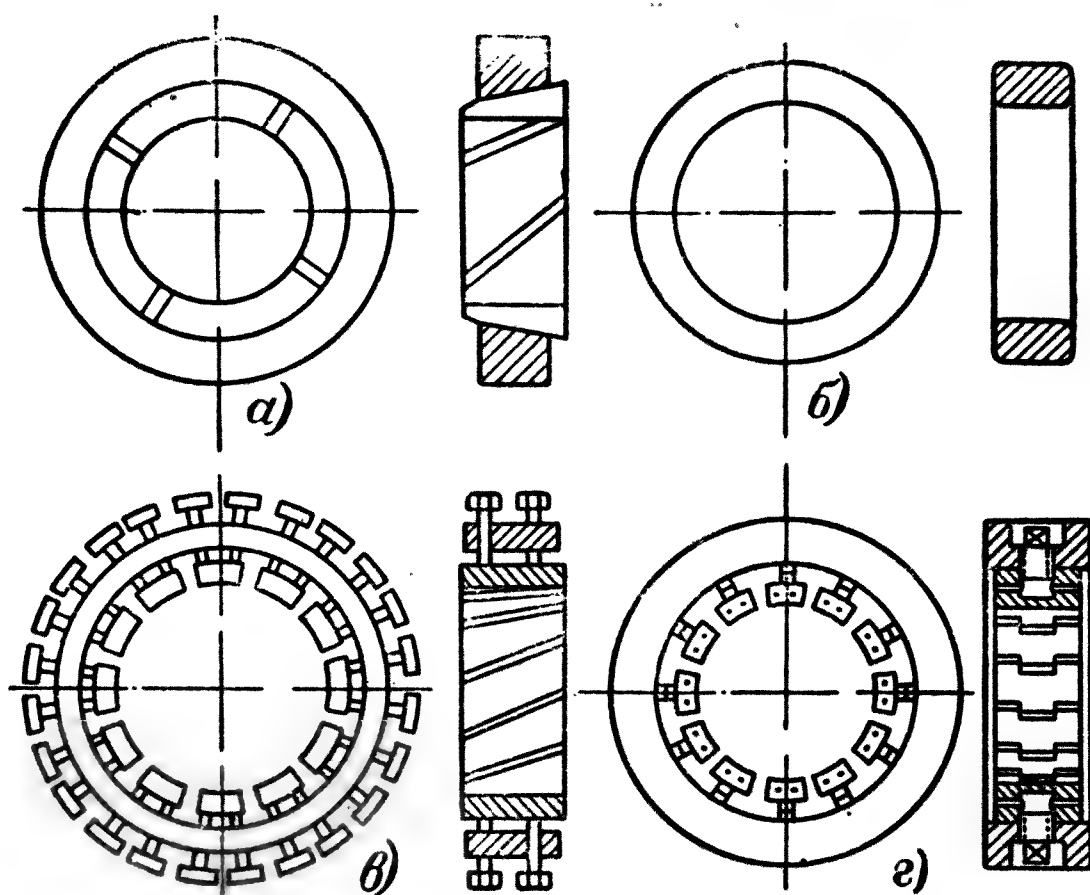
Кольца для прессовки комплекта пластин коллектора.
